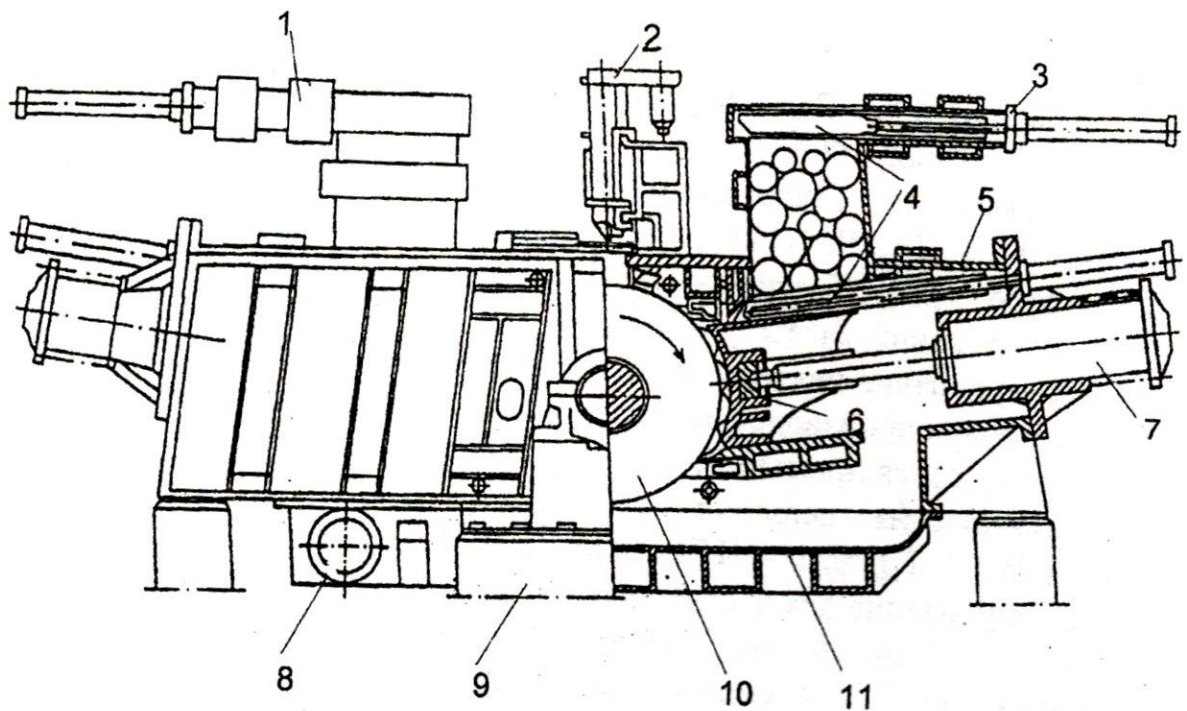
Двухпрессовый дефибрер фирмы «Valmet», работающий под давлением:
